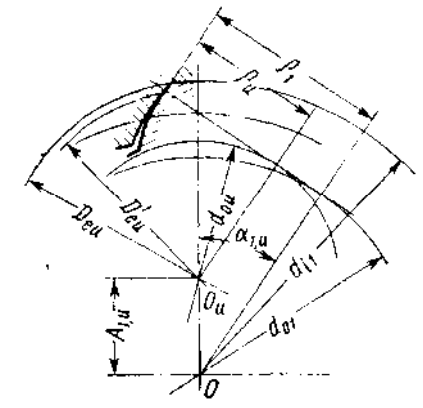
Зацепление долбяка и колеса с внутренними зубьями
